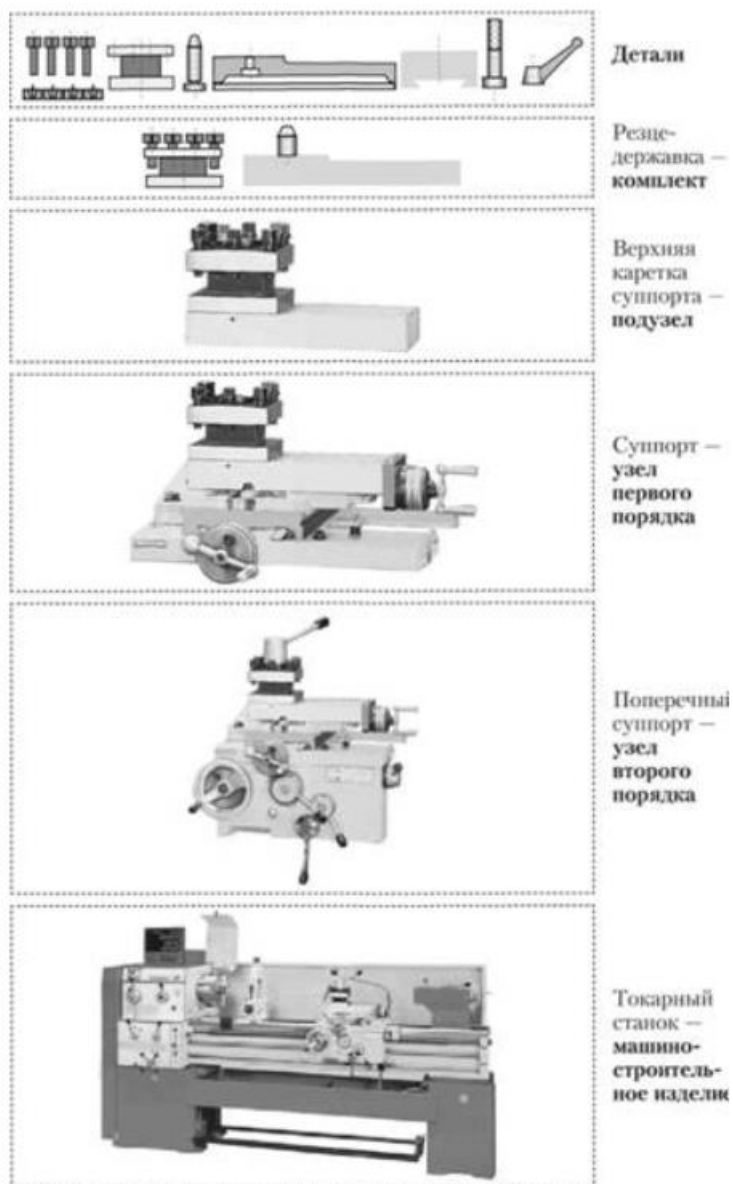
Процесс последовательного образования сборочных единиц и сборочных единиц в станок
